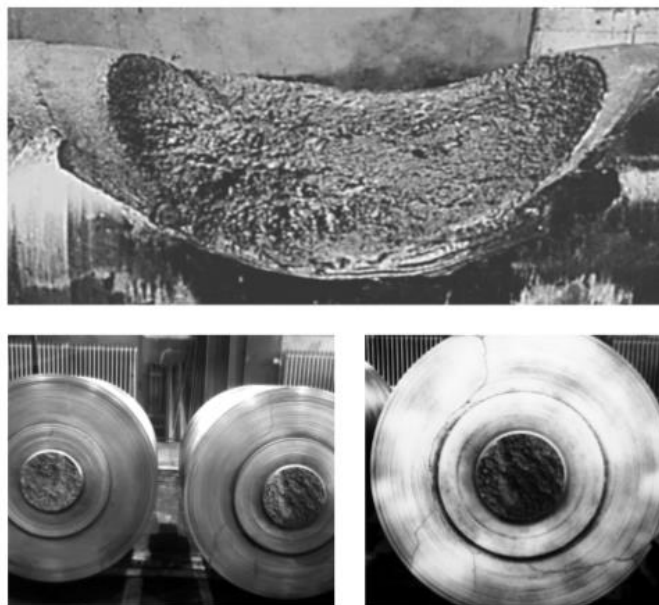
Ejemplo de fractura por fatiga tipo "silla de montar" [44]
